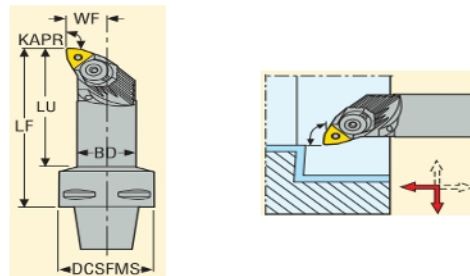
Державка C4-PWLNR/L-13080-06 [1, с. 335]
